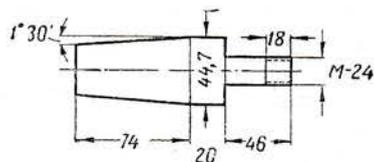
Деталь приспособления для проточки коленчатого вала J1-3/2
